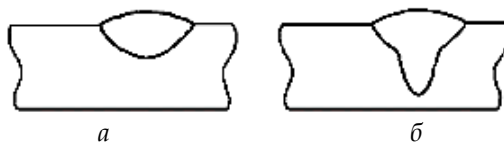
Форма проплавления для обычной (а) и для плазменной (б) дуги
